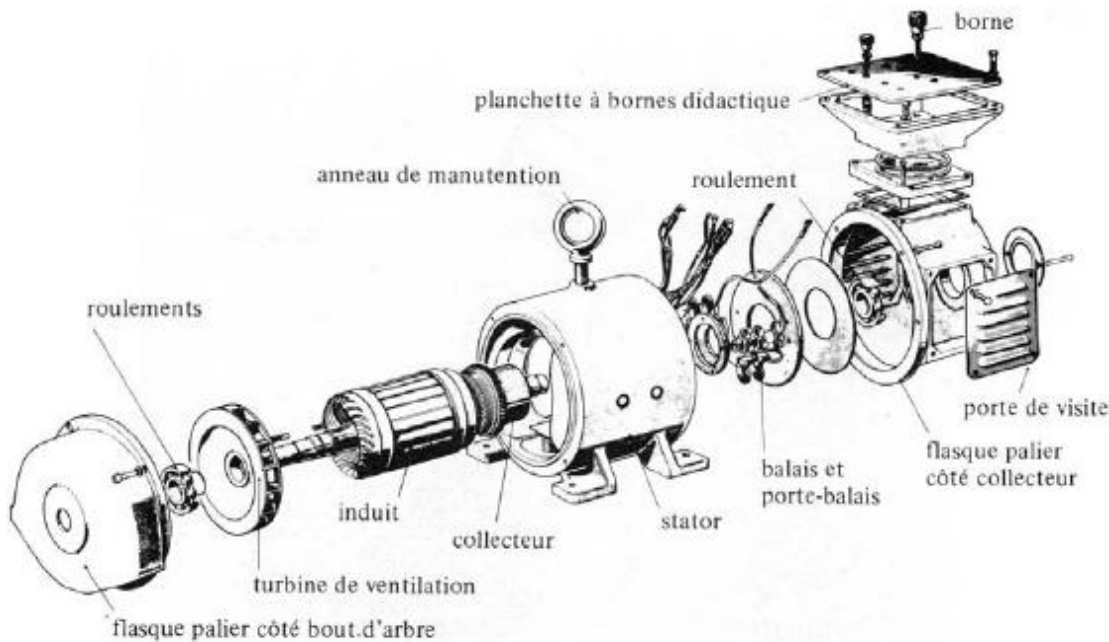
Vue éclatée d'une machine à courant continu. [1]
